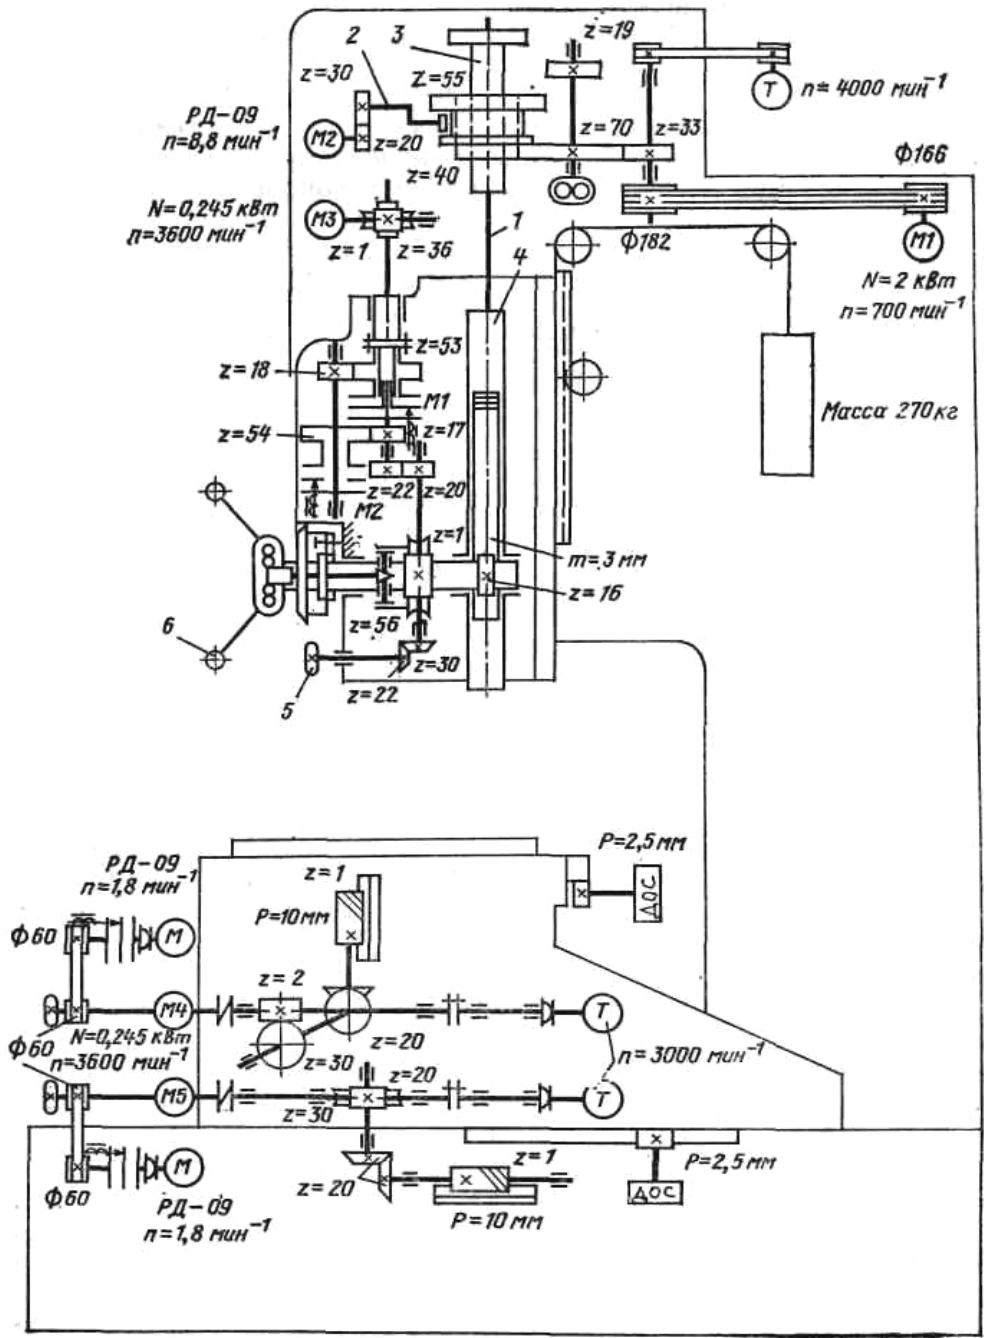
Кинематическая схема координатно-расточного станка модели 2Д45АМФ2
